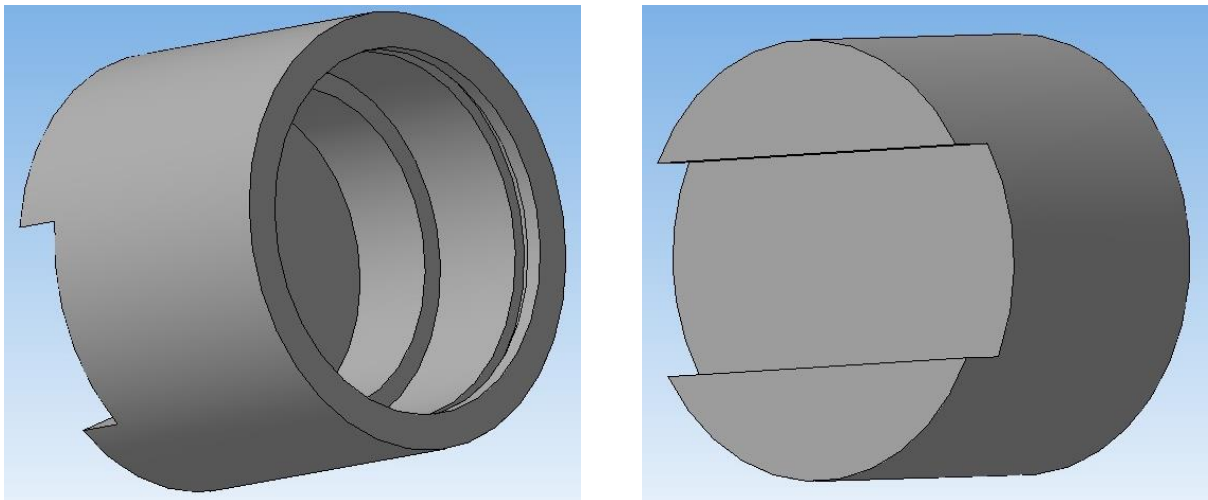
Загальний вигляд деталі «Втулка опорна»
